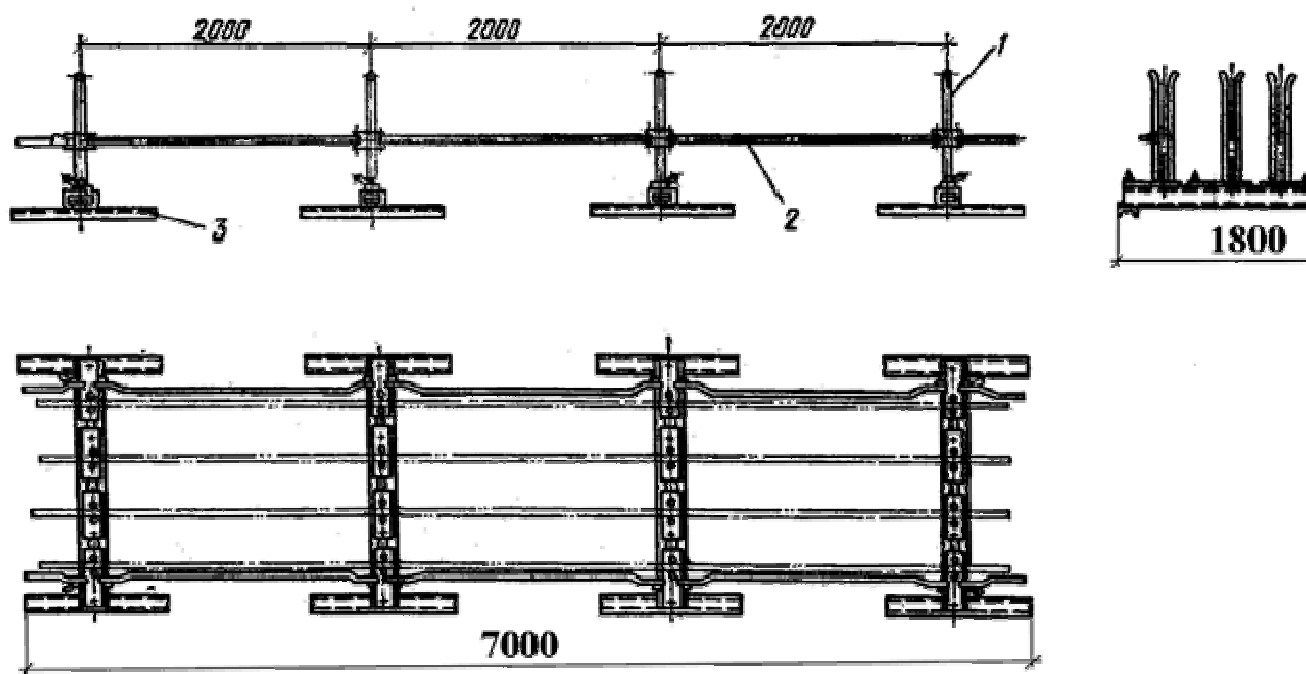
Кондуктор-шаблон для сборки и сварки пространственных арматурных каркасов:
